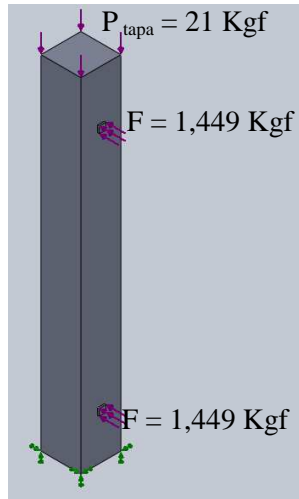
Cargas aplicadas en el soporte de las platinas fijas.
